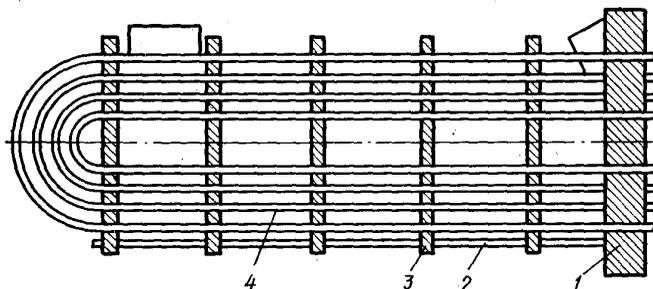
Сборка каркаса U-образного трубного пучка
